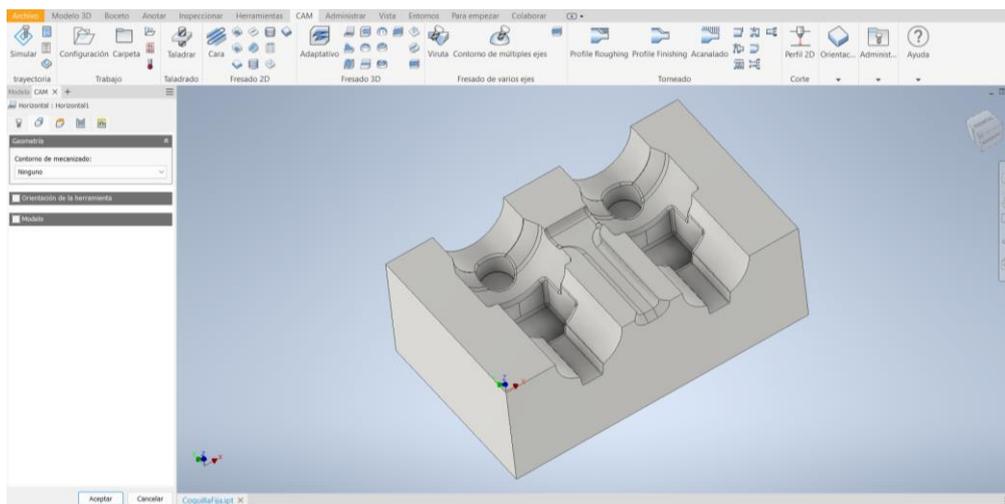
Pestaña “geometría” en estrategia de acabado horizontal
